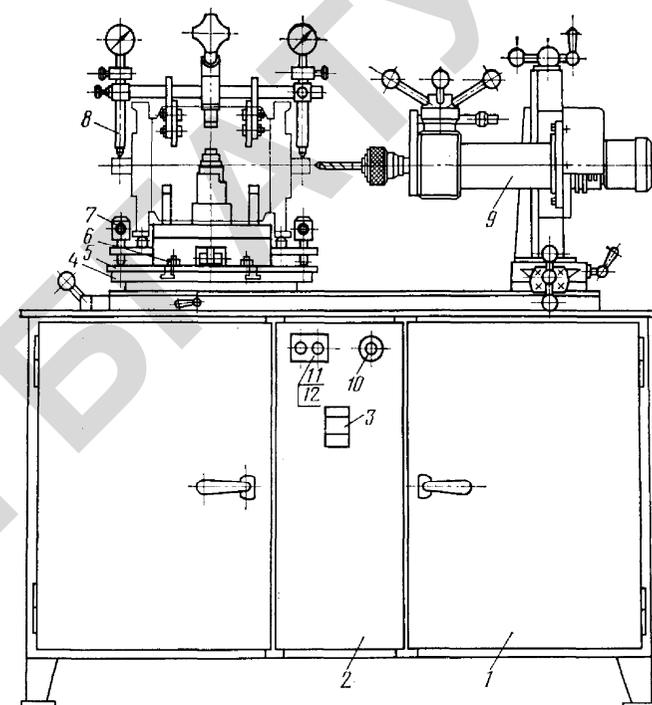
Стенд ОР-9023 для сборки вакуумных насосов: 1 – стол; 2 – панель; 3, 11, 12 – пульт управления; 4 – стол поворотный; 5 – плита; 6 – болт; 7 – винт; 8 – индикаторное приспособление; 9 – сверлильное устройство; 10 – лампочка
